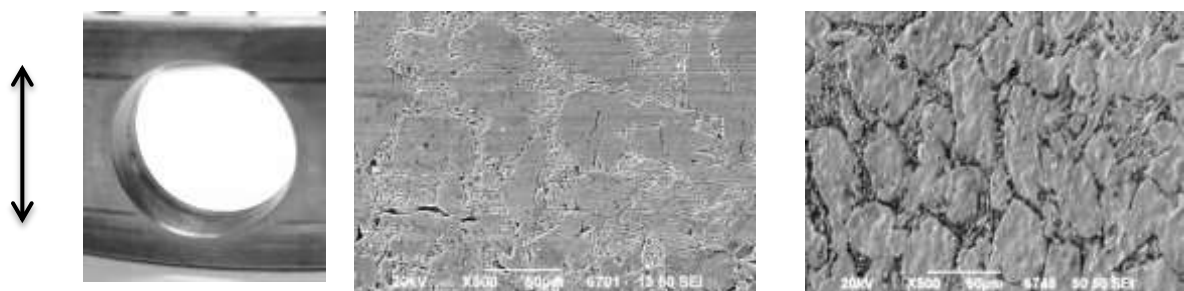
Состояние поверхности сепаратора подшипника № 1
